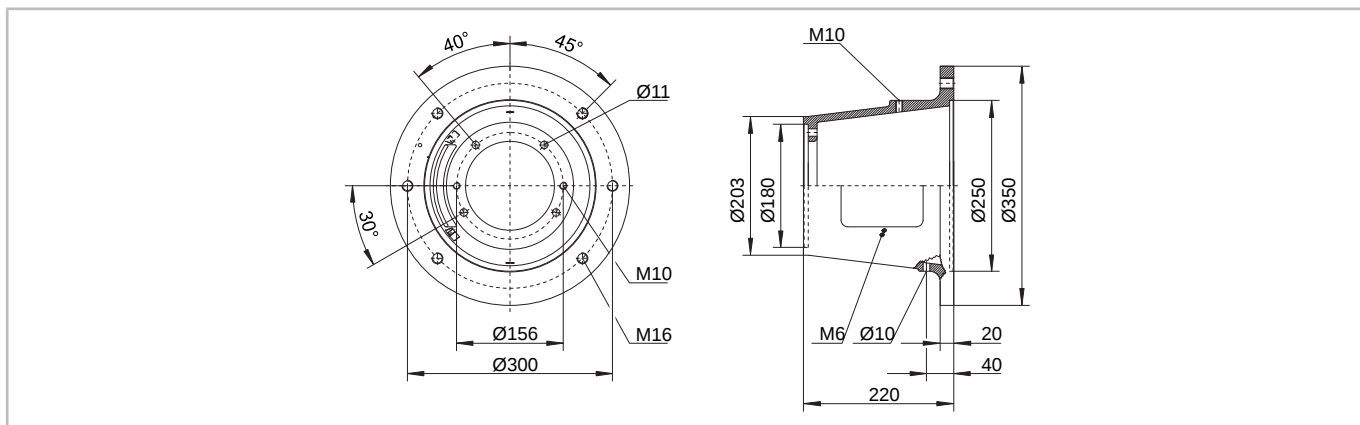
Габаритный чертеж кожуха муфты GS5070
